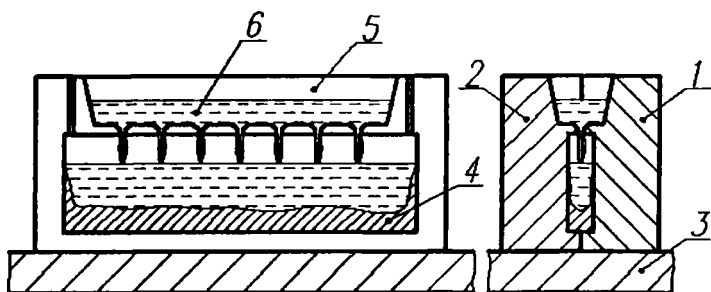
Схема получения заготовок цинковых анодов литьем в кокиль: 1 – полуформа подвижная; 2 – полуформа неподвижная; 3 – плита; 4 – отливка; 5 – литниковая система; 6 – жидкий металл
